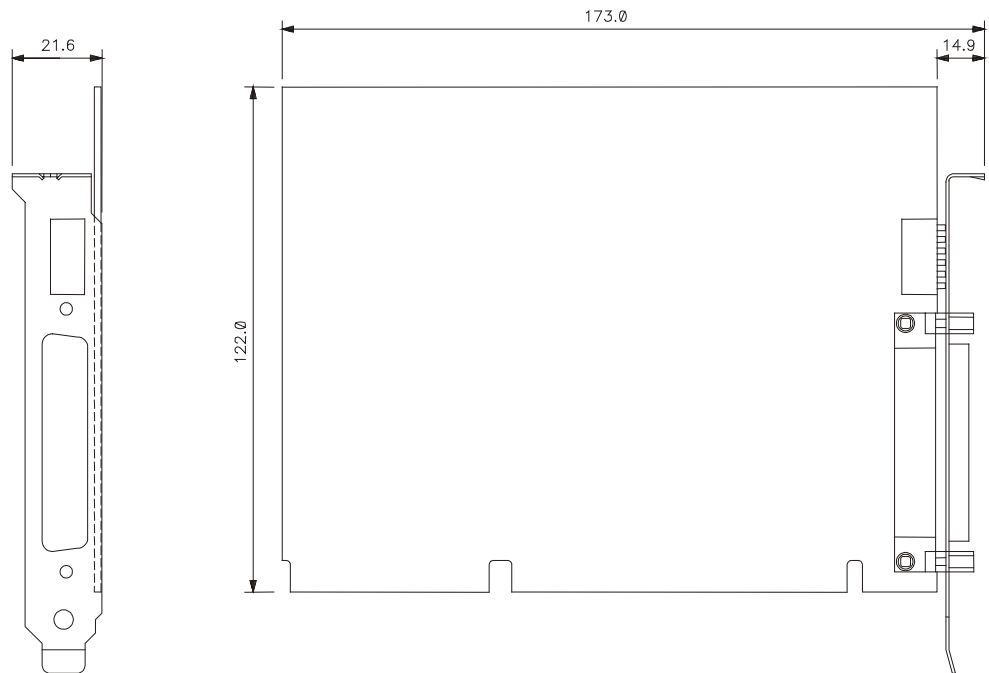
Dimensões Físicas do Cartão PCI302 V1.1x (mm)
